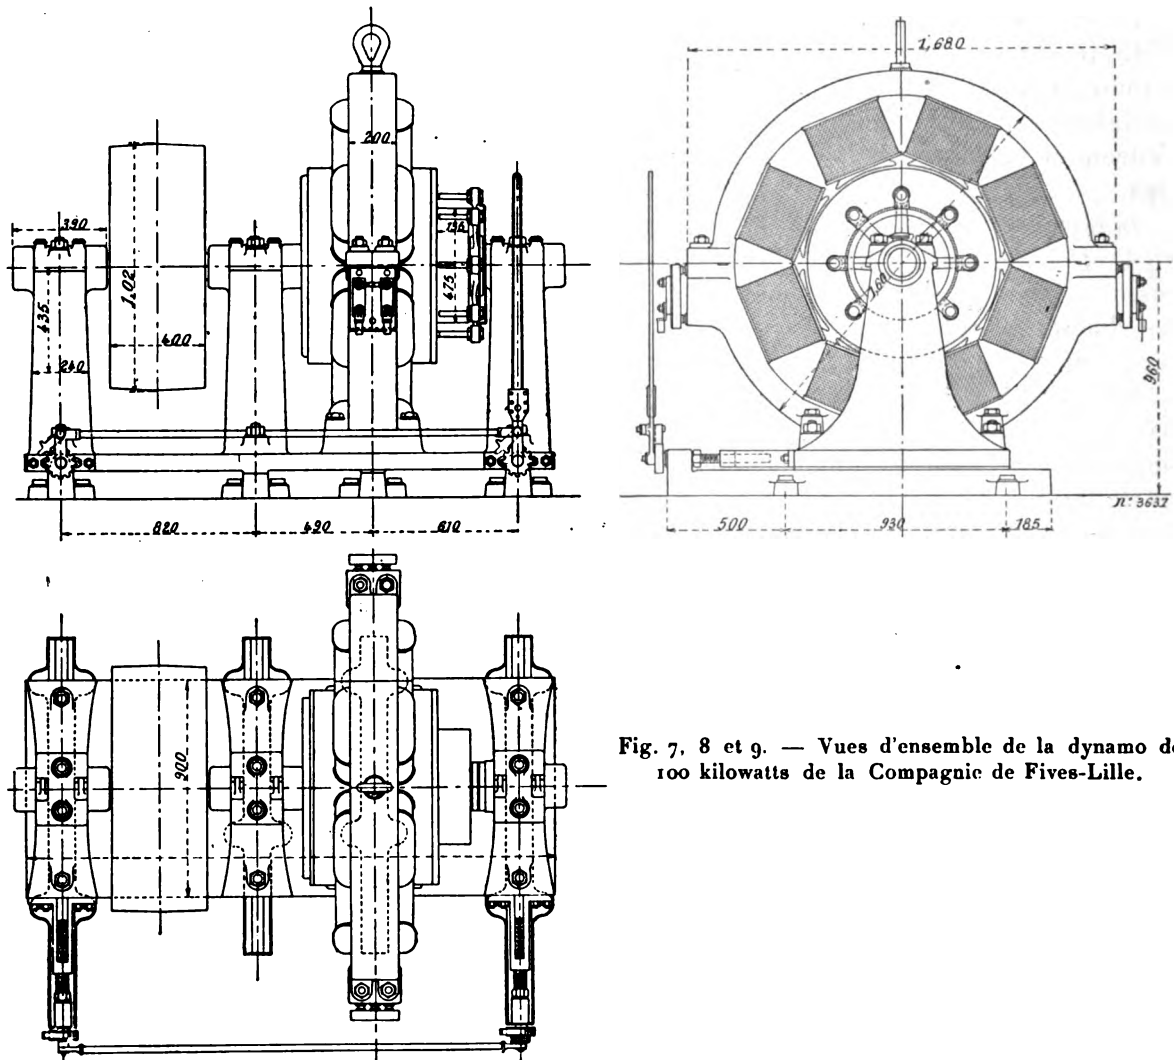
, 8 et 9. — Vues d'ensemble de la dynamo de 100 kilowatts de la Compagnie de Fives-Lille.
